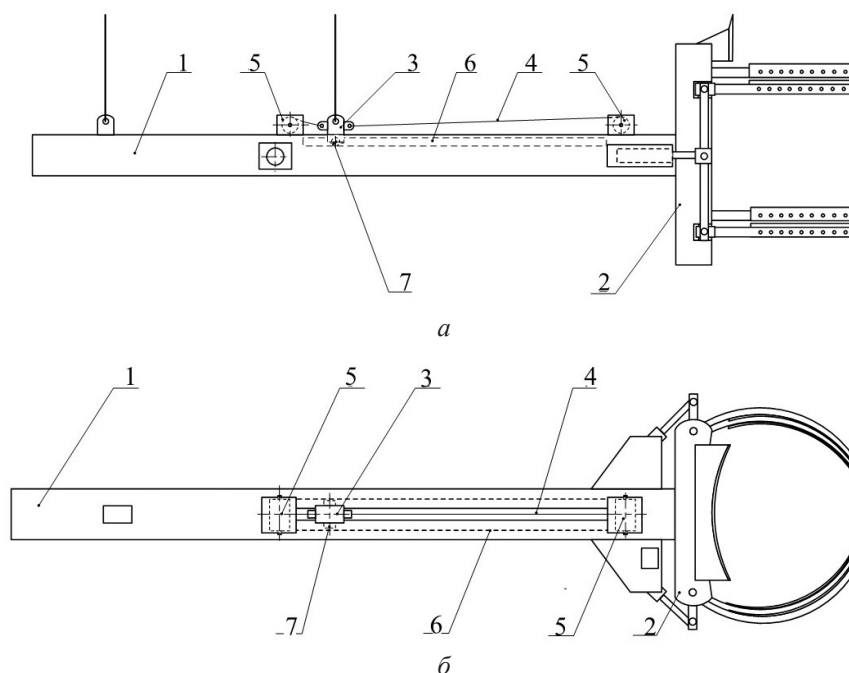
Конструкция ОГЗМ ВТД: *а* – вид сбоку; *б* – вид сверху
